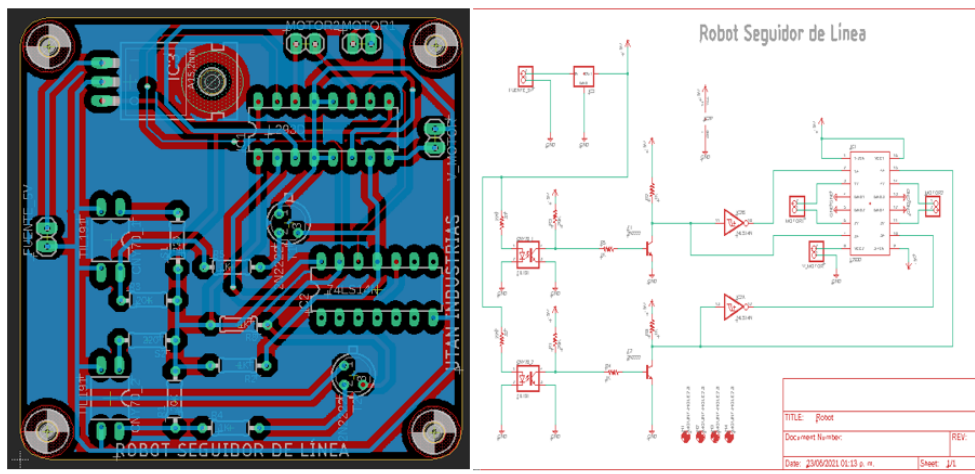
Esquema y PCB final de la electrónica de control desarrollada para el robot seguidor de línea.
